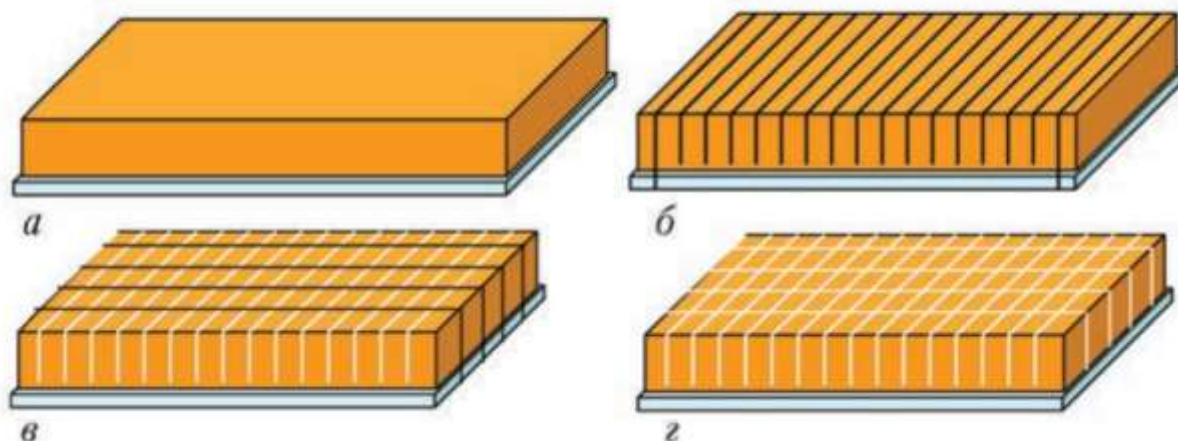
Покрокові ескізи технології виготовлення багатоелементних сцинтиляційних збірок: а - сцинтиляційна заготовка, наклеєна на підкладку; б - сцинтиляційна заготовка, що прорізає на 16 каналів; в - сцинтиляційних заготовка, розрізана на 1D-матриці; г - 2D-матриця, виготовлена для цифрової радіографії.
